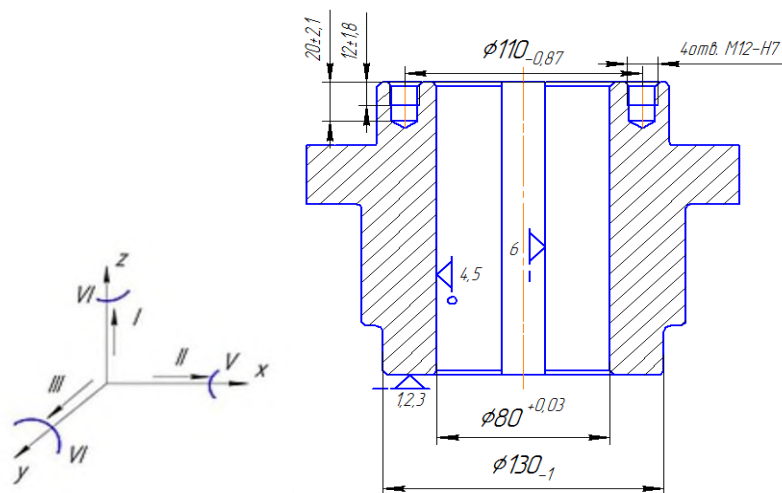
Схема базування деталі на операції 070 Свердлування
